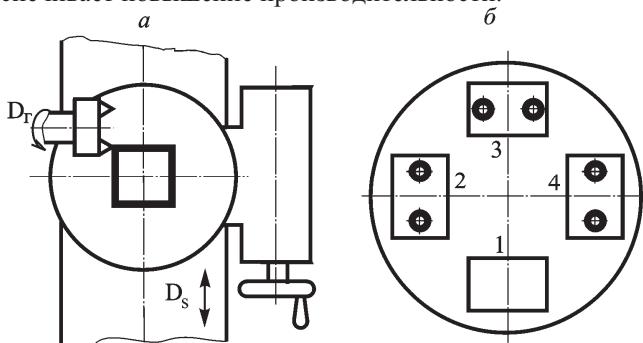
Четырехпозиционная обработка сторон квадрата (а) и отверстий корпуса (б)
